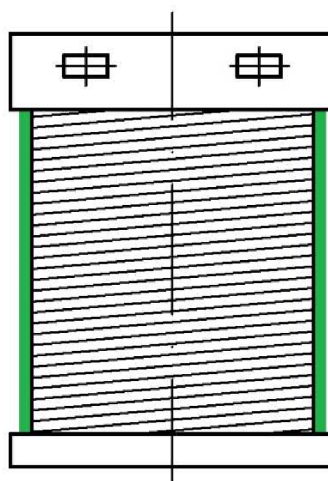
Vinutí prostupující po zapouzdření povrchem pouzdra.
